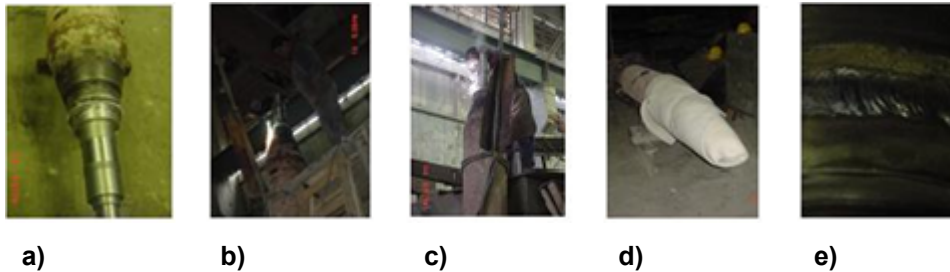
Vistas de diferentes momentos del proceso de soldadura.
